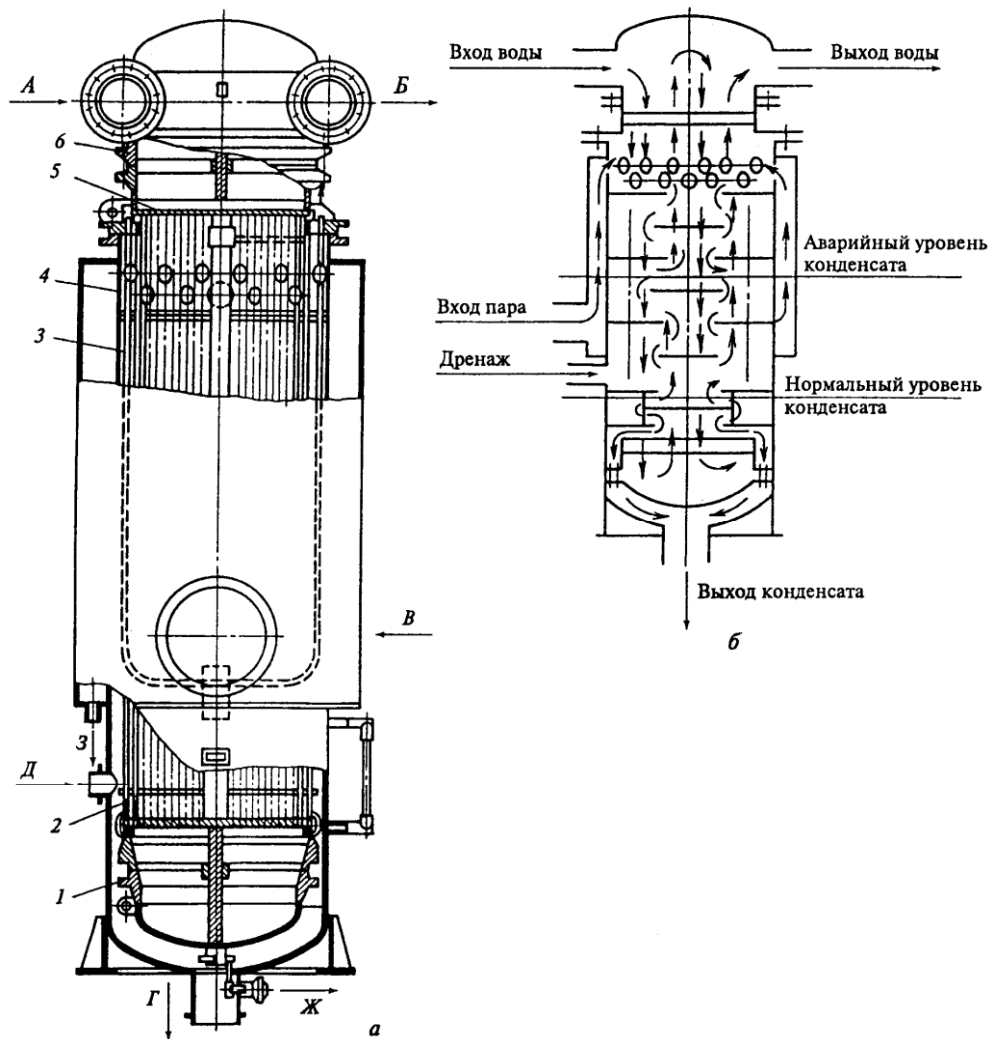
Регенеративный подогреватель низкого давления ПН-1800-4,2-0,4-1А: *a* – общий вид; *б* – схема движения пара и воды; *A, Б* – вход и выход нагреваемого конденсата; *B* – вход греющего пара; *Г* – отвод конденсата греющего пара; *Д* – вход конденсата греющего пара из подогревателя более высокого давления; *E* – отсос паровоздушной смеси; *Ж* – опорожнение трубной системы; *З* – отвод конденсата из паровой камеры; *1* – нижняя водяная камера; *2* – перегородки трубной системы; *3* – трубки; *4* – корпус; *5* – трубная доска; *б* – верхняя водяная камера
